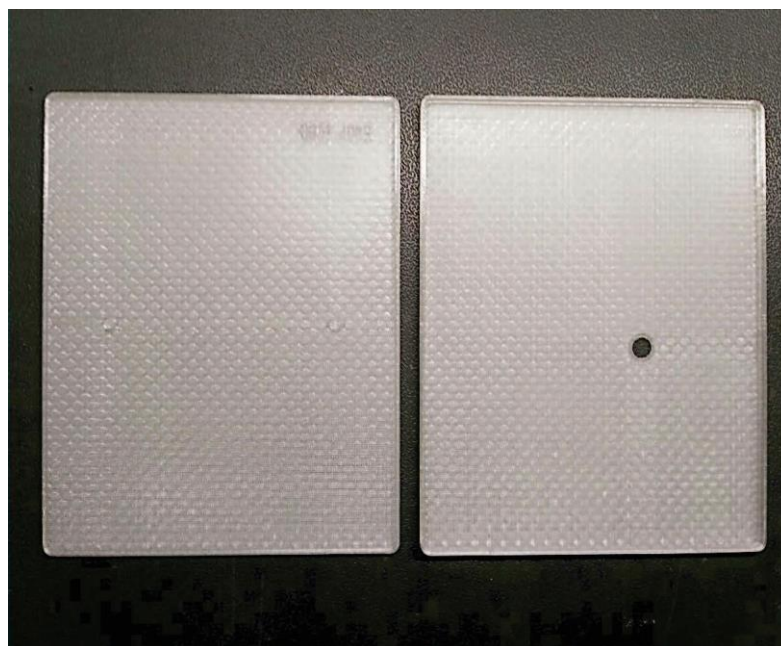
Внутрішній вигляд роздрукованого корпуси
